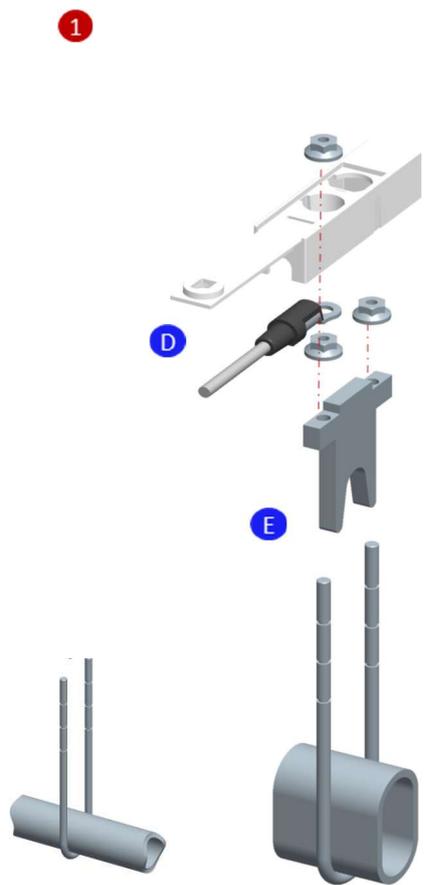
Montage Konvektorbügel mit Fernfühler komplett
